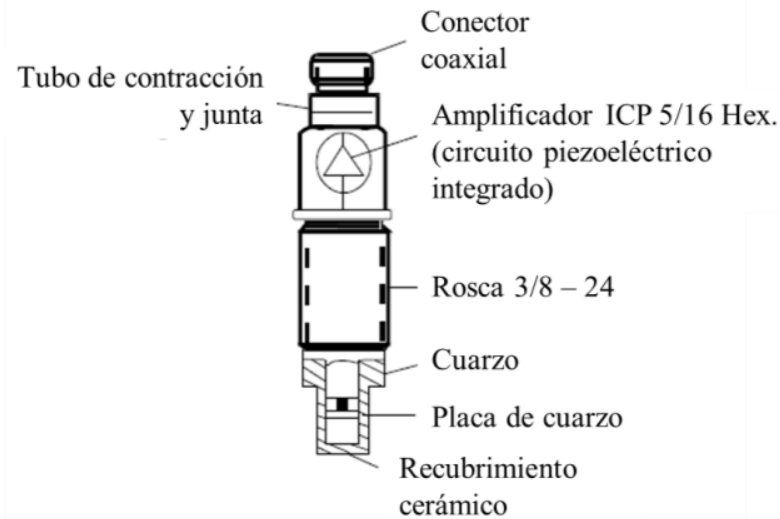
1. Esquema del sensor de presión de inyección tipo PCB108
